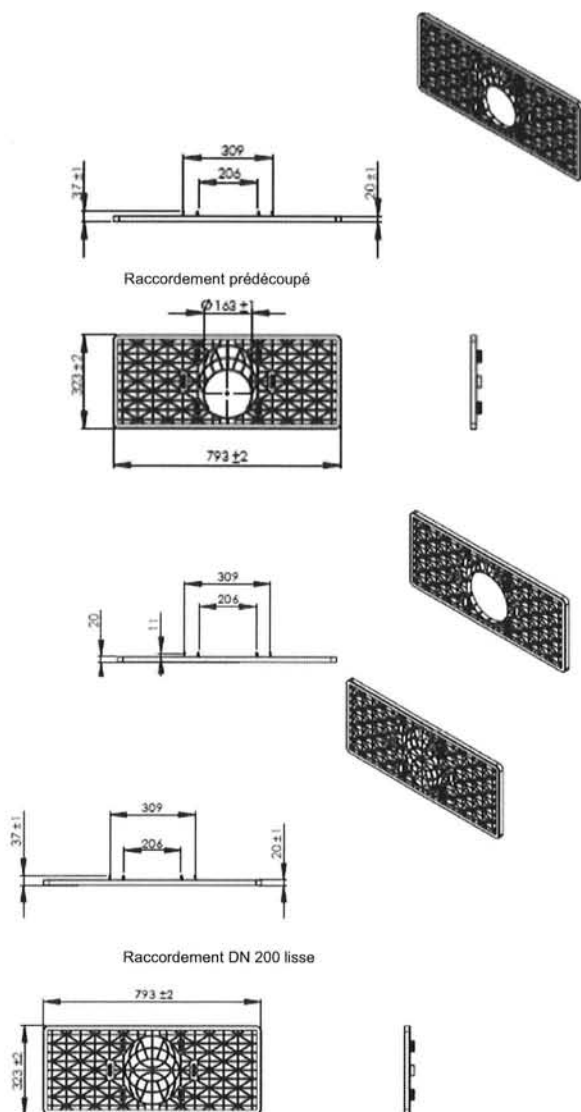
Plaque d'about et plaque d'about ajourée ouverture DN 150 ou DN 200
